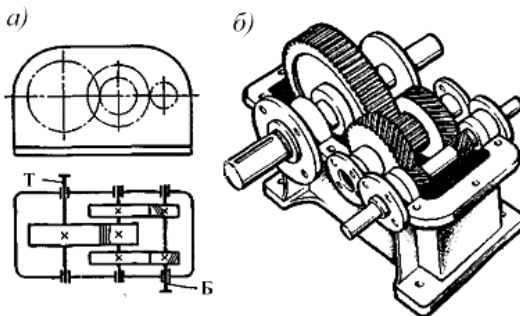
Цилиндрический двухступенчатый горизонтальный редуктор с раздвоенной первой (быстроходной) ступенью:
